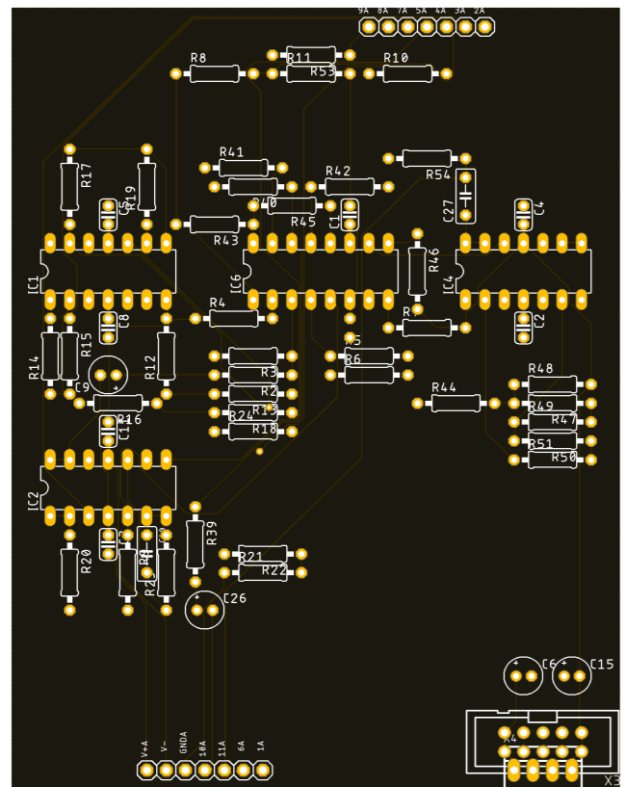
Board Layout: Pots&Sockets PCB
